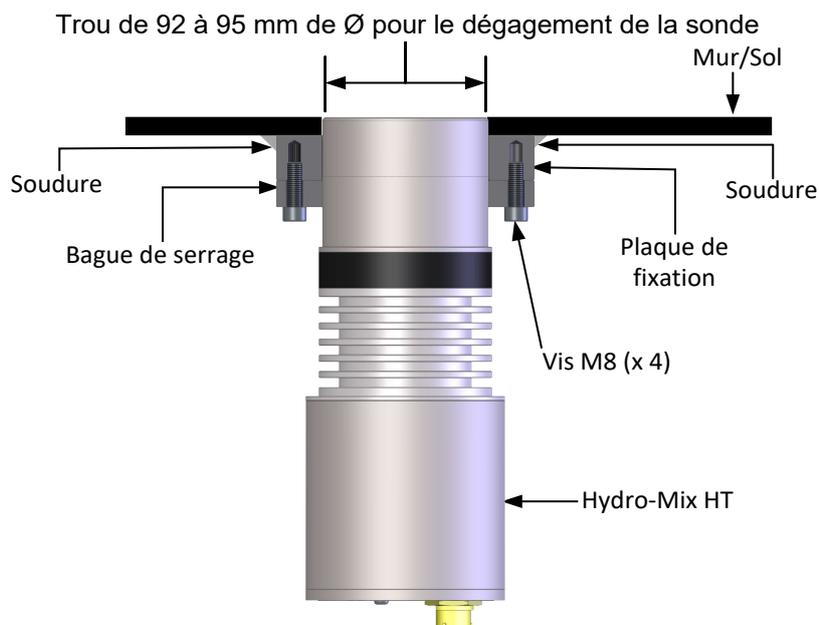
Installation de la sonde (Plaque de fixation installée de l'extérieur)
